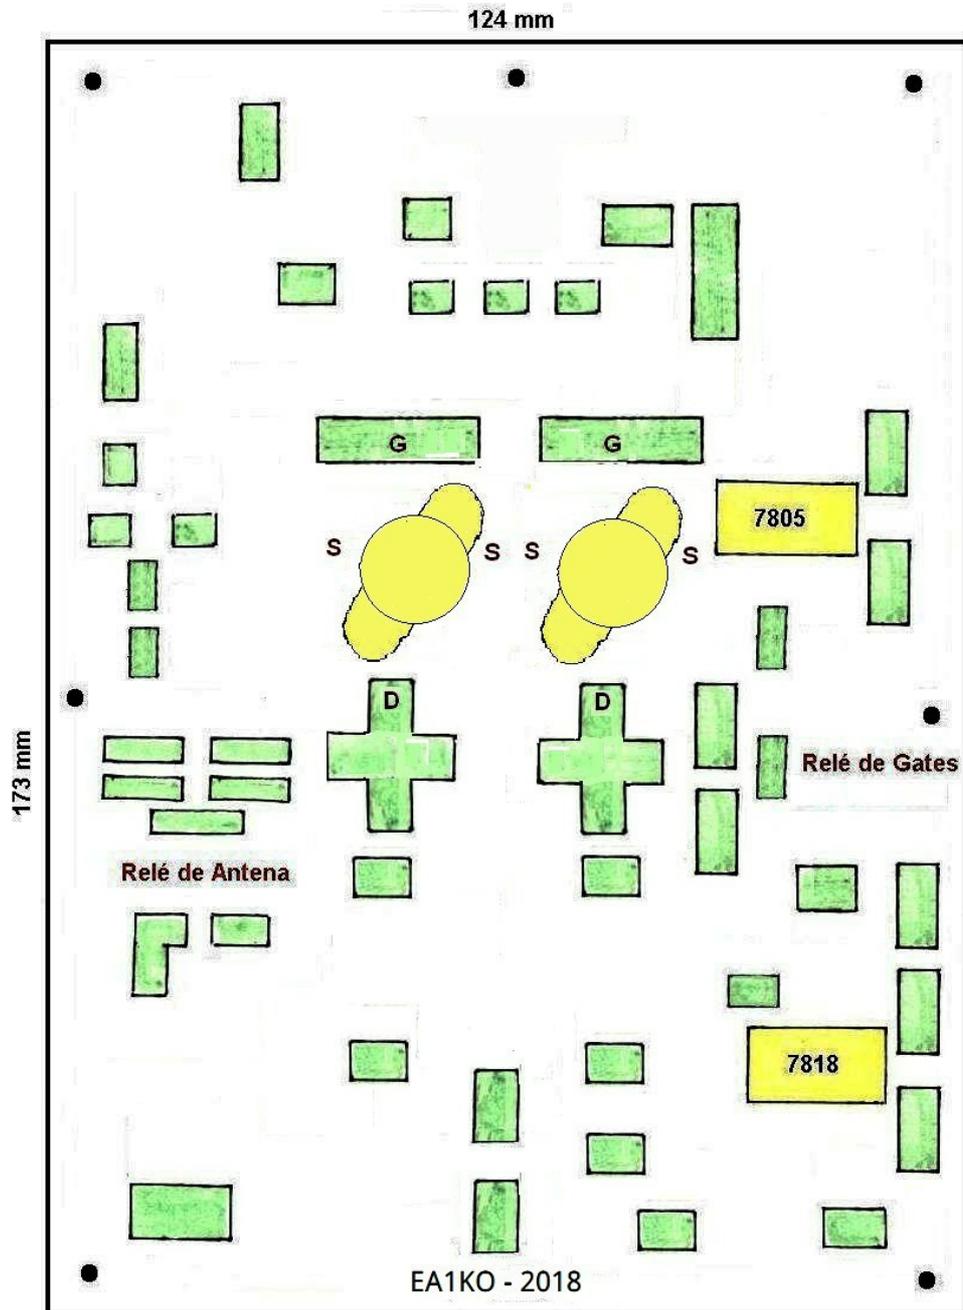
Detalles constructivos y disposición práctica de los componentes.
